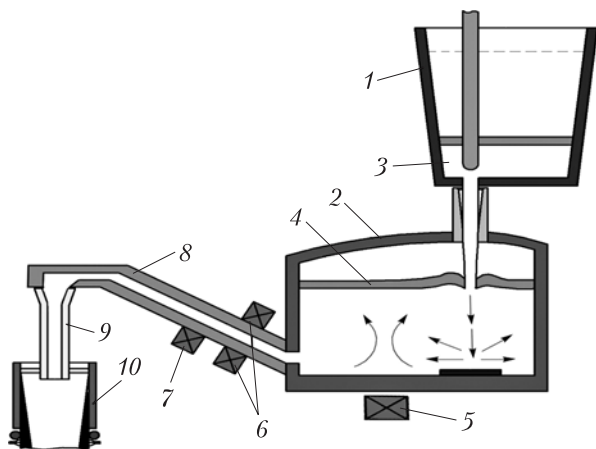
Общий вид промежуточного ковша для микро-МНЛЗ с применением устройств, реализующих комплекс электромагнитных воздействий: 1 – сталеразливочный ковш; 2 – промежуточный ковш; 3 – жидкая сталь; 4 – покровный шлак; 5 – электромагнитный перемешиватель; 6 – электромагнитный индуктор для подогрева стали; 7 – электромагнитное устройство для дозирования стали при разливке; 8 – огнеупорный канал для транспортировки стали; 9 – погружной стакан; 10 – кристаллизатор МНЛЗ
